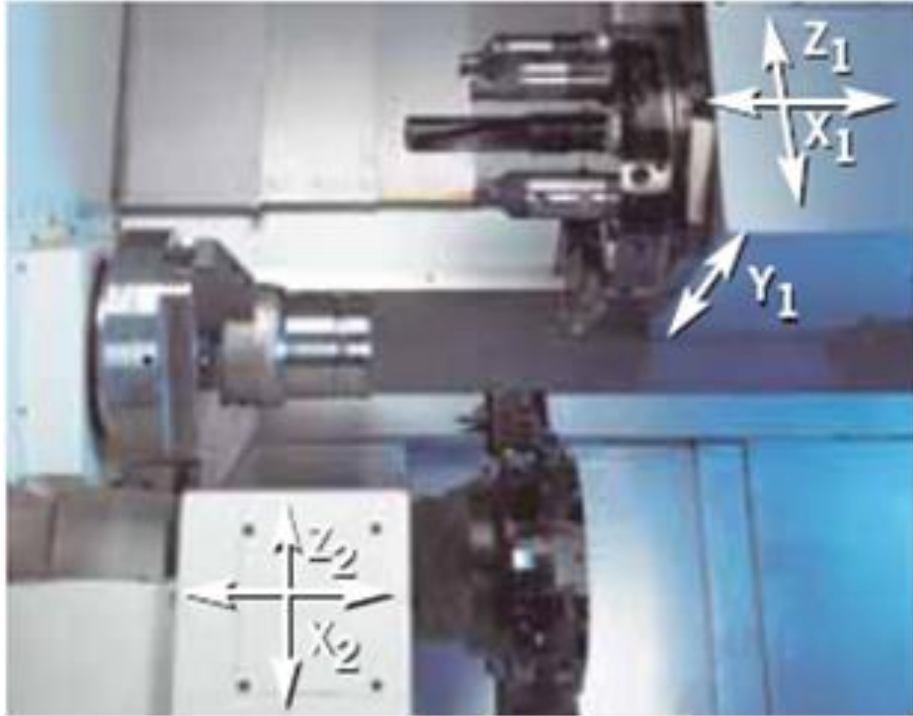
Робоча зона та системи координат токарного верстата з револьверною головкою
